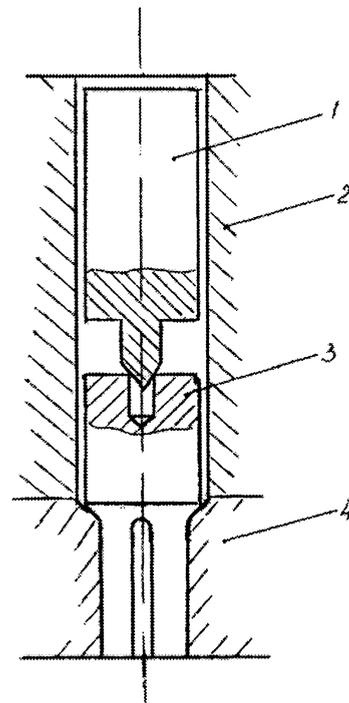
Схема выдавливания биметаллического инструмента: 1 – хвостовик; 2 – контейнер; 3 – заготовка; 4 – матрица
